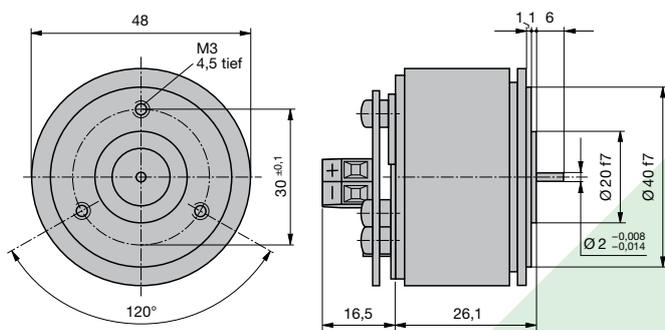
KINAX 2W2 mit Standard-Antriebswelle nur vorn, Ø 2 mm, Länge 6 mm. Anschlussvariante mit Schraubklemmen.
